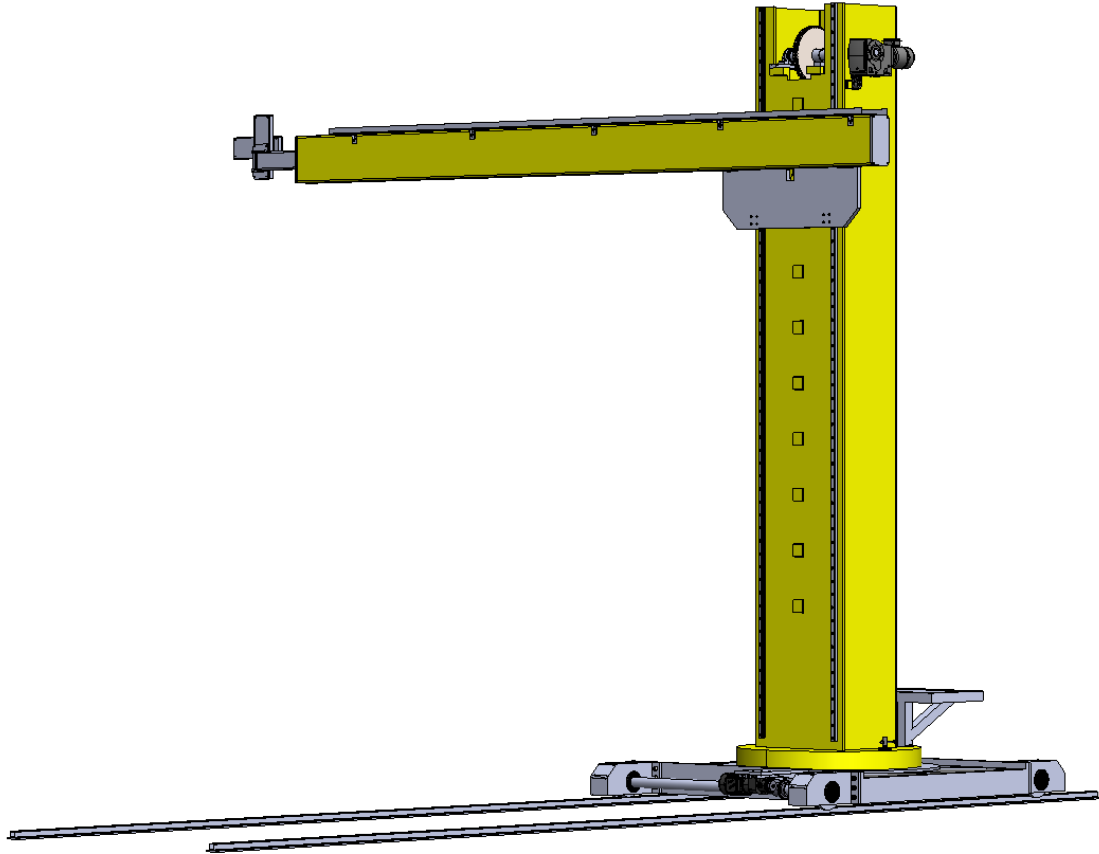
Conjunto geral da coluna de soldadura
